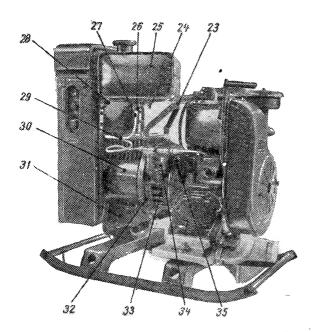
Агрегат без кожуха: 23 — болт, крепящий топливный бак на генераторе; 24 — сливная пробка бака; 25 — топливный бак; 26 — проходной кран; 27 — накидная гайка бензопровода; 28 — болт, крепящий бак на блоке аппаратуры; 29 — бензопровод; 30 — генератор; 31 — болты, крепящие генератор к раме; 32 — гайка, крепящая соединительный фланец на генераторе; 33 — соединительный фланец; 34 — фильтр-отстойник; 35 — гайка, крепящая фильтр-отстойник
